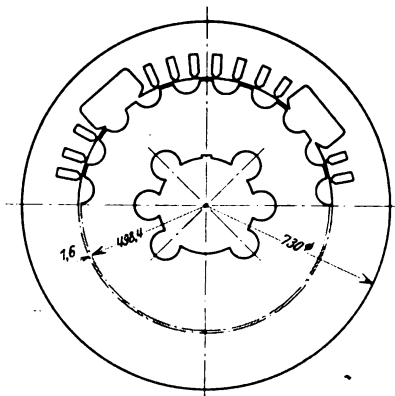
Stator- und Rotorblechnschnitt der 100 kW-Maschine.
